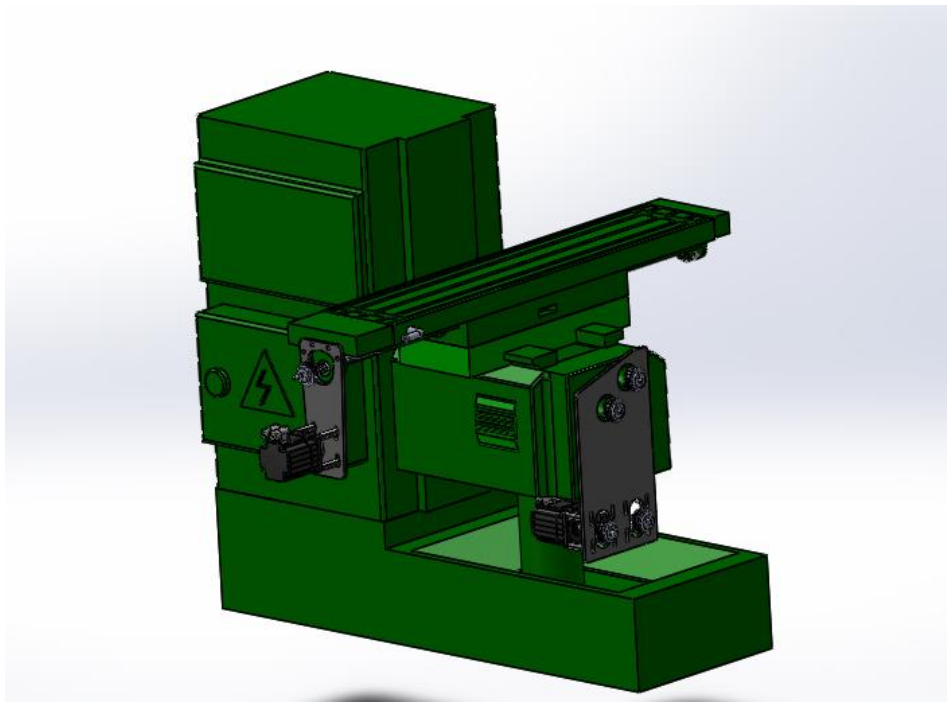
Vue 3D de la modélisation complète de la machine.
